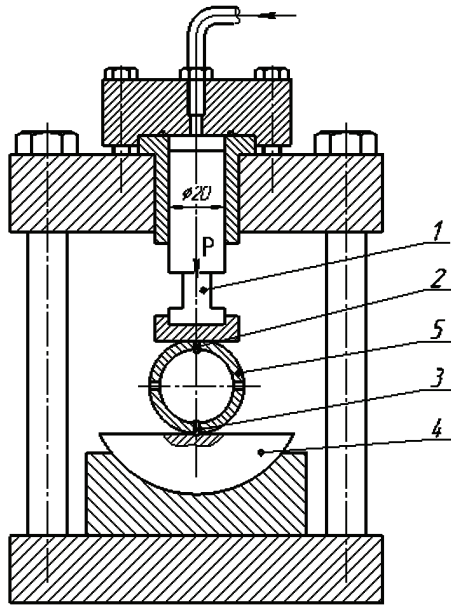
Приспособление для испытаний втулки ПГШ:
